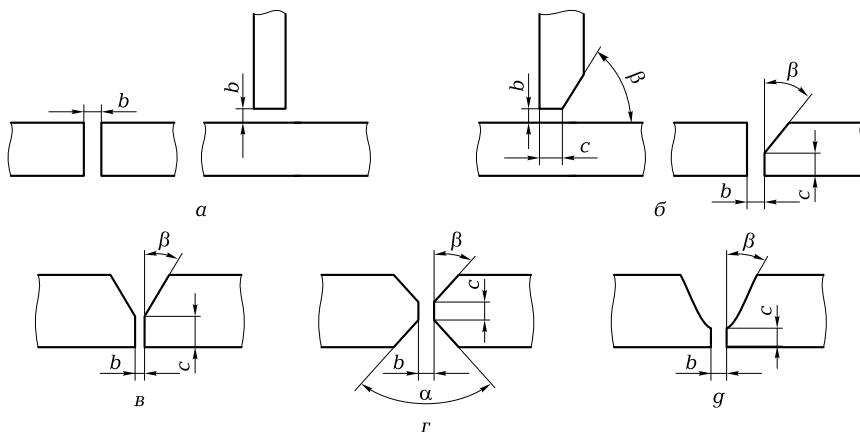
Конструктивные элементы разделки кромок под сварку
